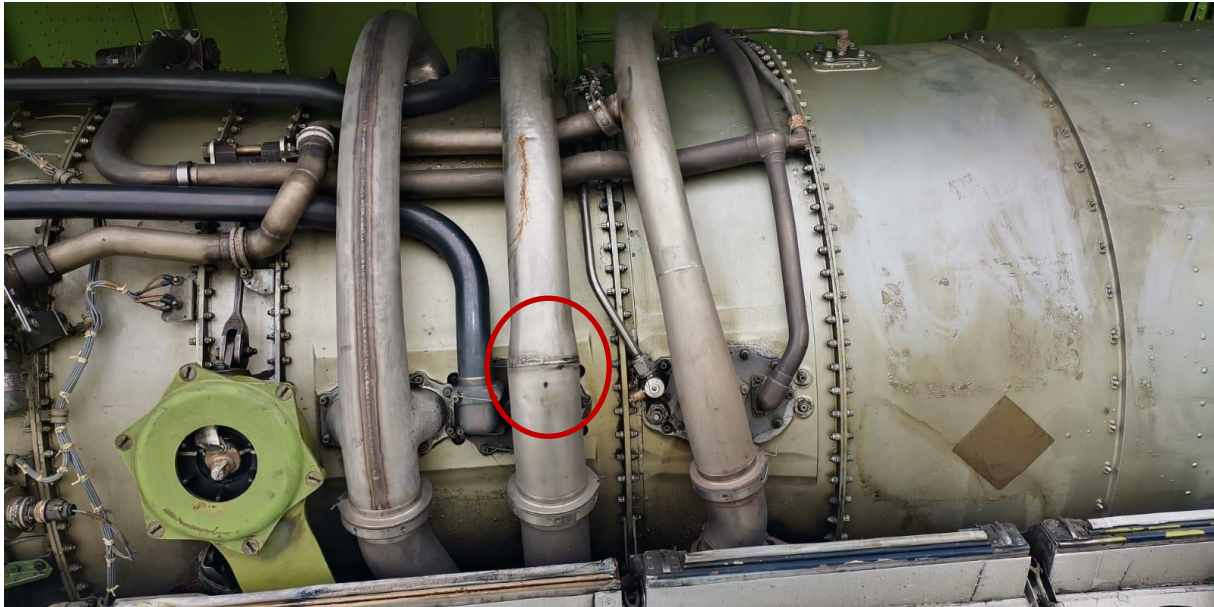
Vista superior del motor 3, indicando el lugar de la fisura.
